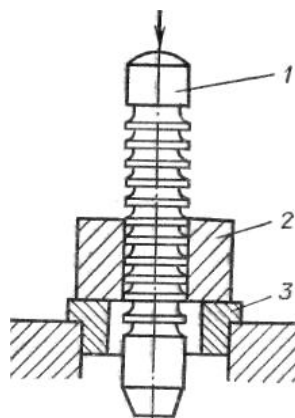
Схема прошивки отверстия: 1 – прошивка (инструмент); 2 – обрабатываемая деталь; 3 – упорная втулка.
